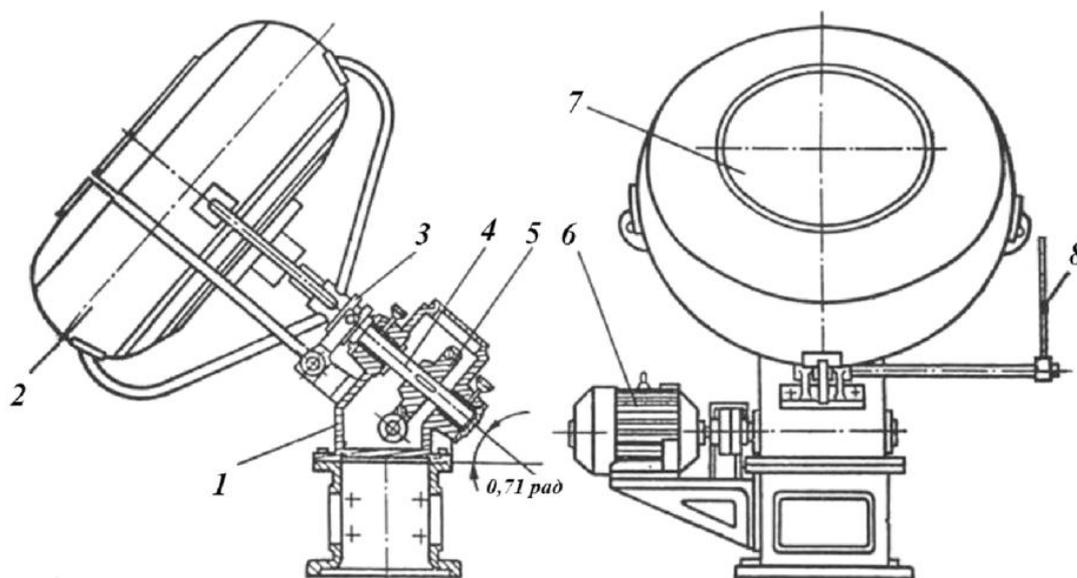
Дражировочная установка с гладкой внутренней поверхностью рабочего барабана: 1 – станина; 2 – рабочий барабан; 3 – муфта сцепления; 4 – наклонный вал; 5 – редуктор; 6 – электродвигатель; 7 – загрузочное отверстие; 8 – рукоятка для переключения частоты вращения вала
